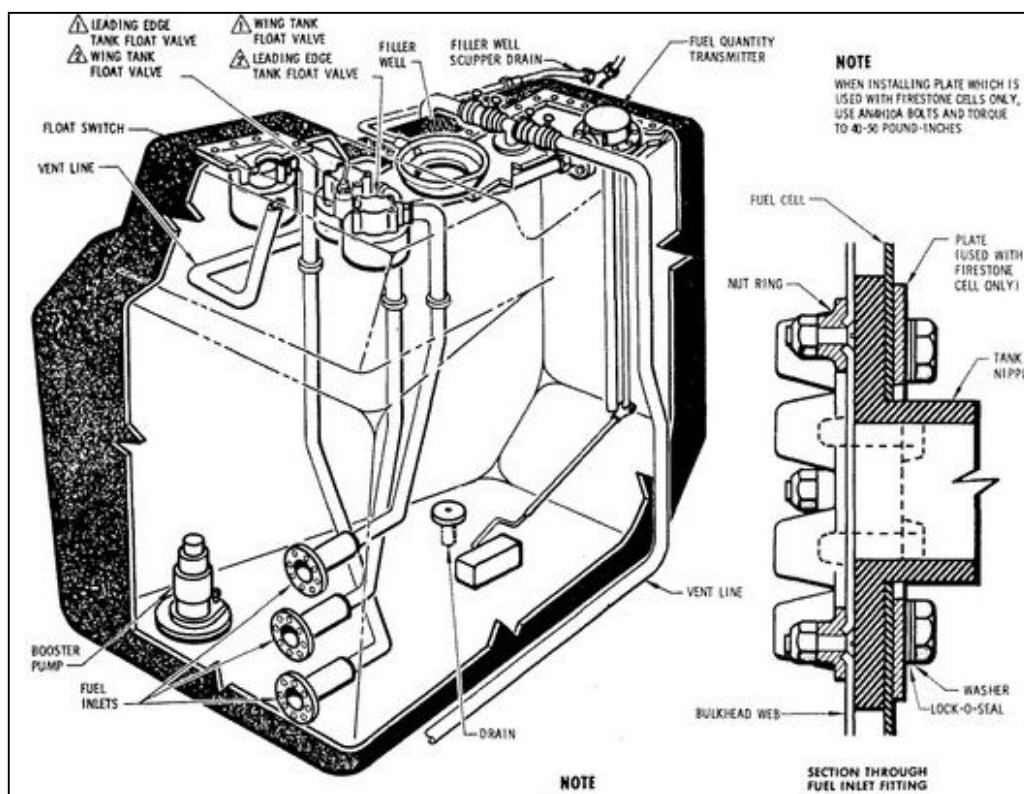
Tanque de combustible del fuselaje del avión T-33.
